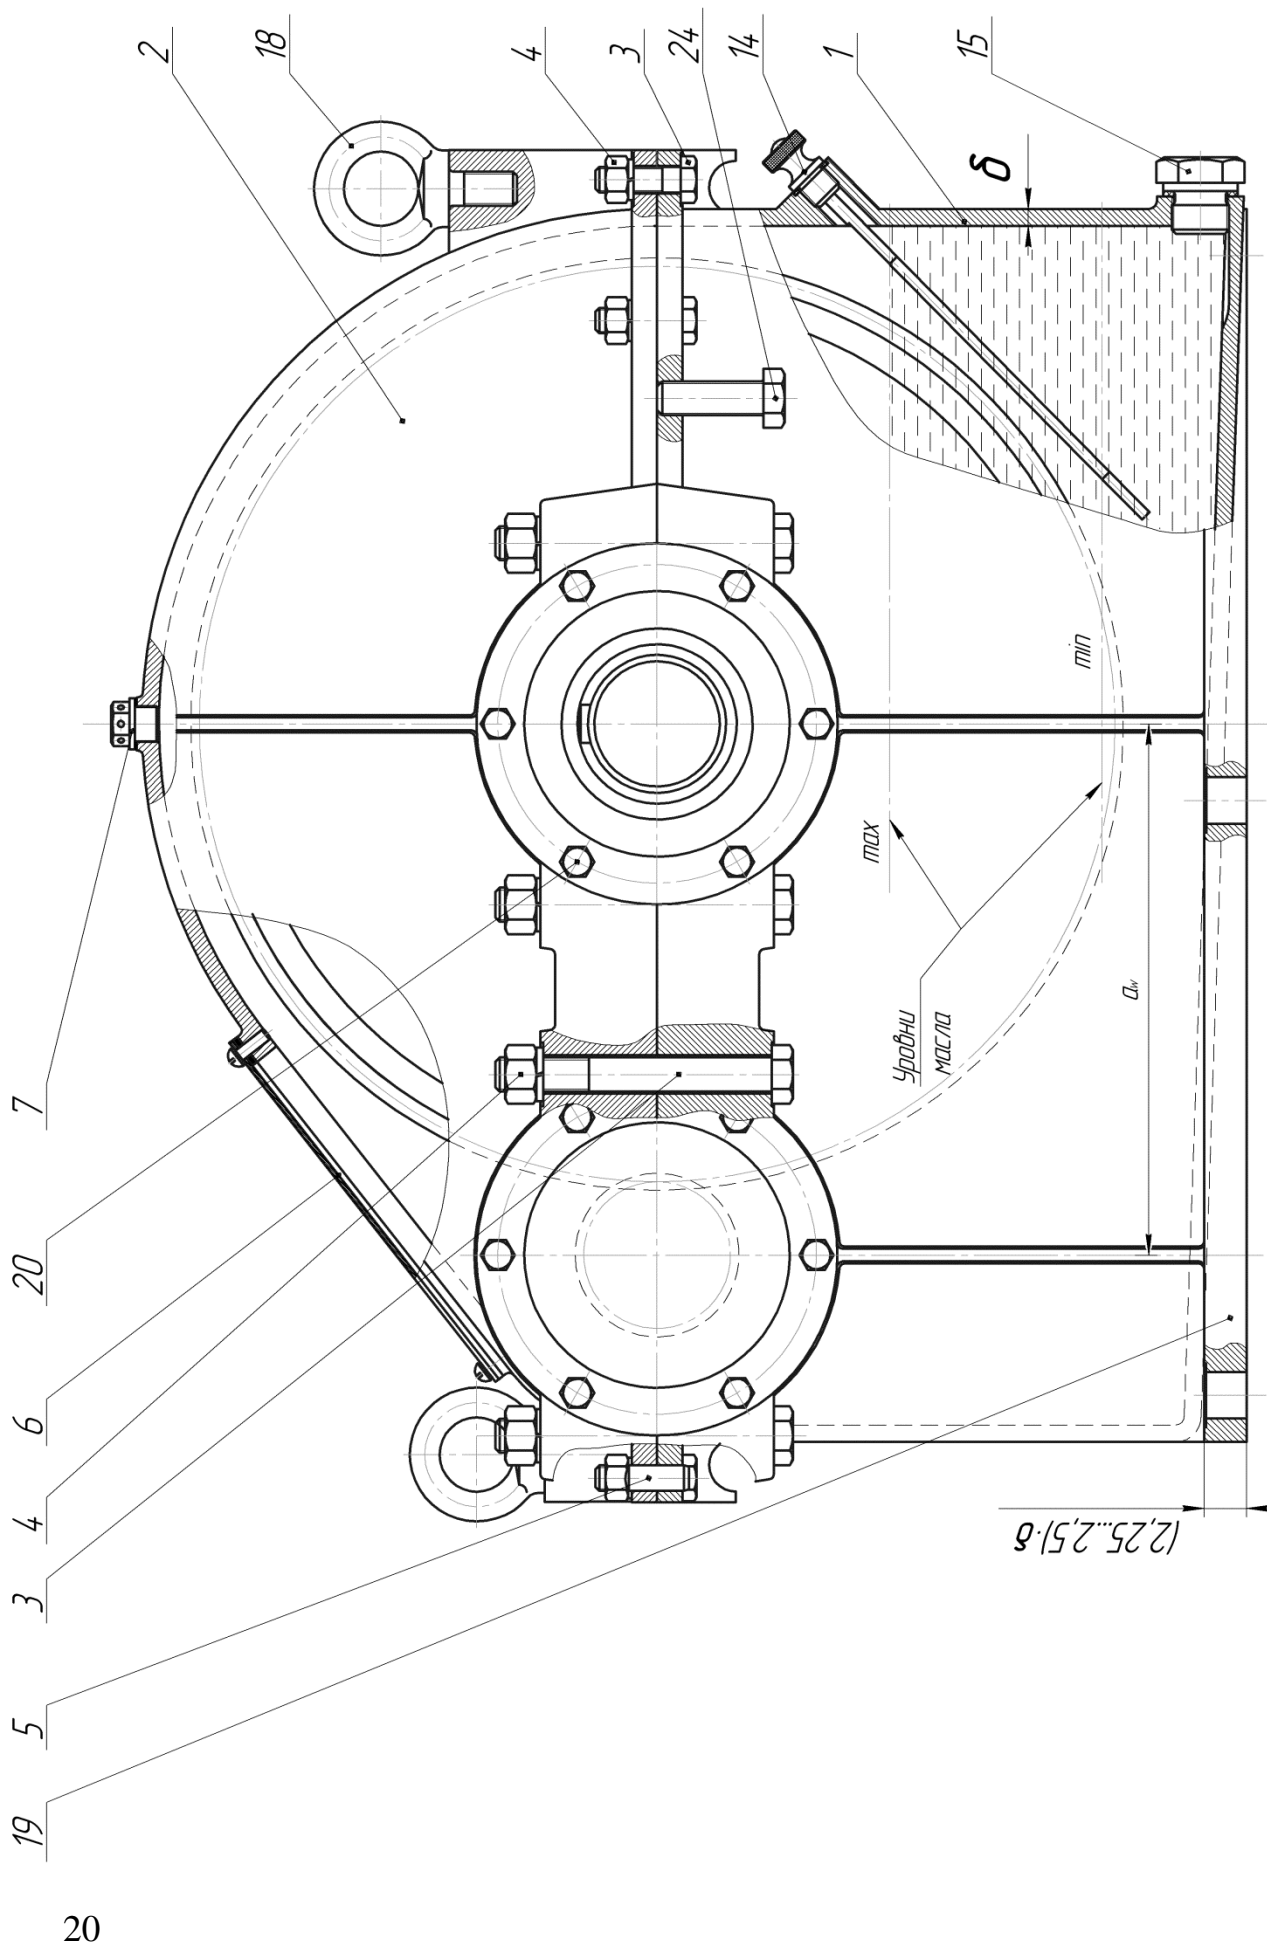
| Конструкция одноступенчатого цилиндрического редуктора (главный вид)
